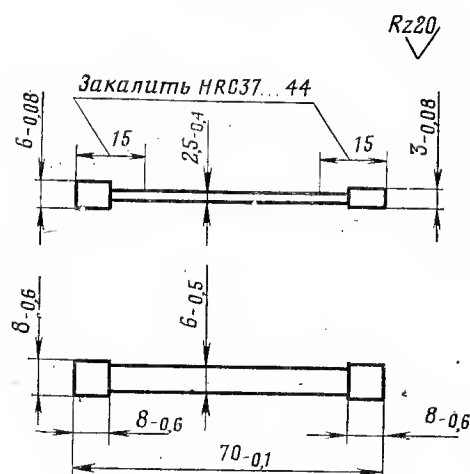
Шаблон для проверки спуска курка с боевого взвода
